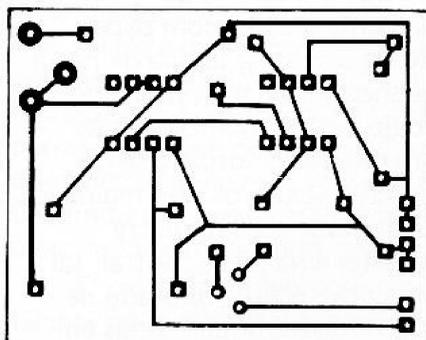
Desenho, em tamanho natural, da plaqueta de circuito impresso vista pelo lado cobreado.
